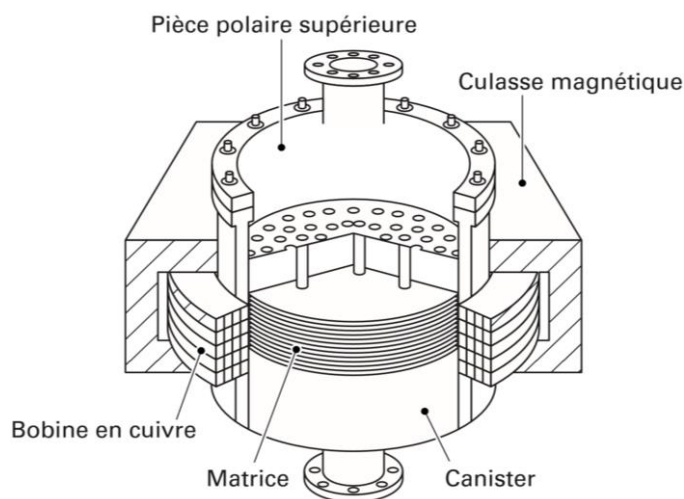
Séparateur magnétique à haut gradient à bobinage de cuivre [Gillet 2004].
